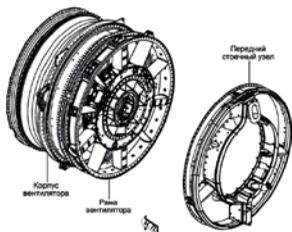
Корпус, рама вентилятора и передний стоечный узел
